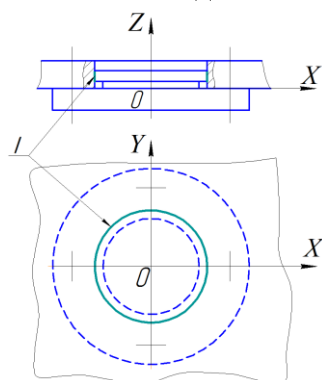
Схема базирования с двойной опорной базой: *I* – двойная опорная база детали; *I* – деталь
